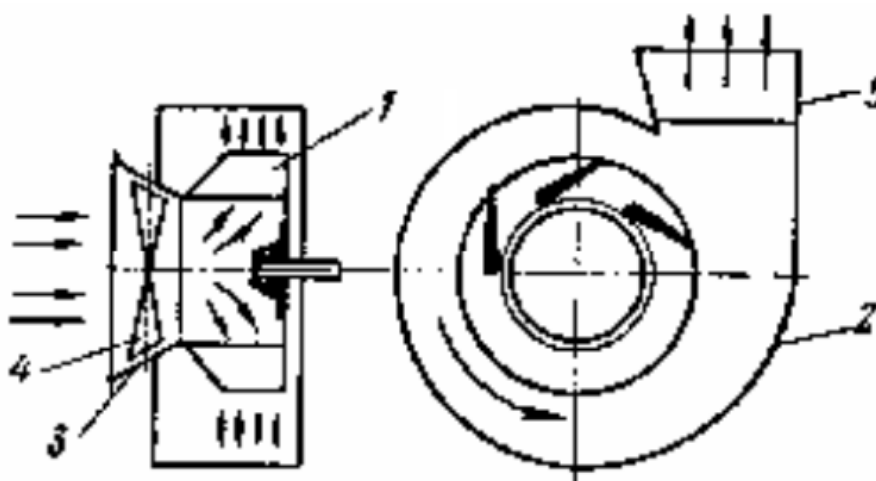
Схема центробежного вентилятора: 1– рабочее колесо; 2 – спиральный кожух; 3 – входной коллектор; 4 – лопатки направляющего аппарата; 5 - диффузор
